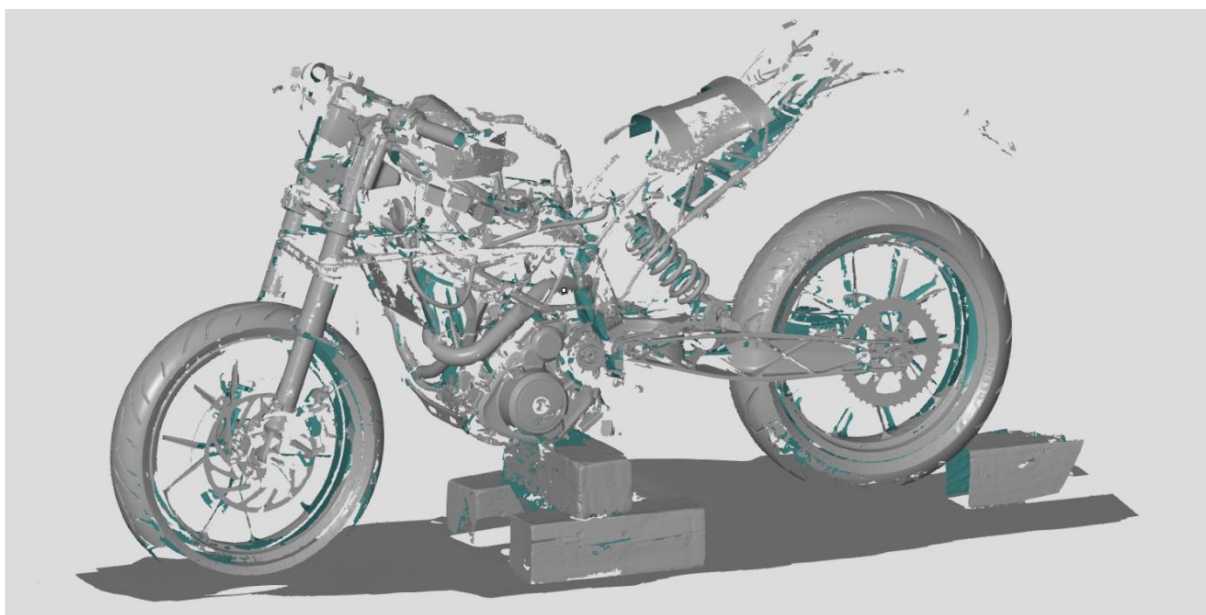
KTM RC 390, 3D skenování, pohled 1
